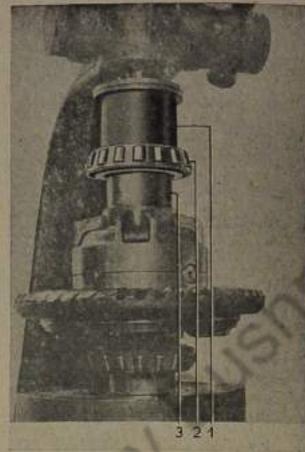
Kegelrollenlager auf Ausgleichgehäuse aufpressen
